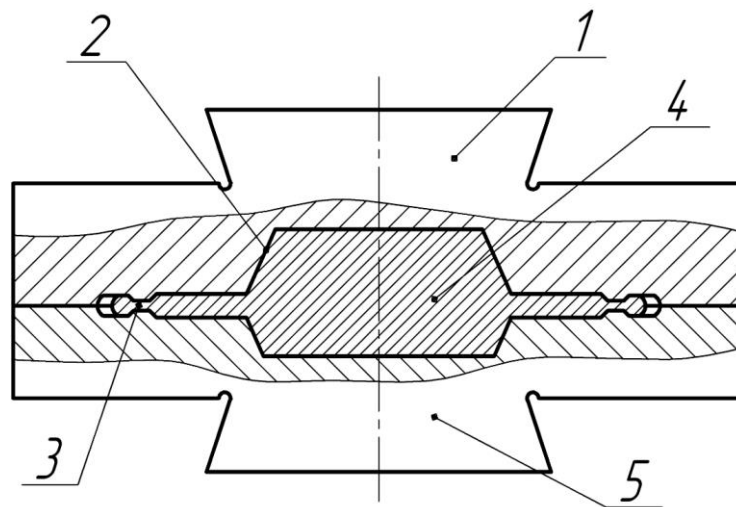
Схема молотового відкритого штапу: 1 – верхня матриця; 2 – стінка рівчика (порожнина); 3 – облой; 4 – поковка; 5 – нижня матриця
